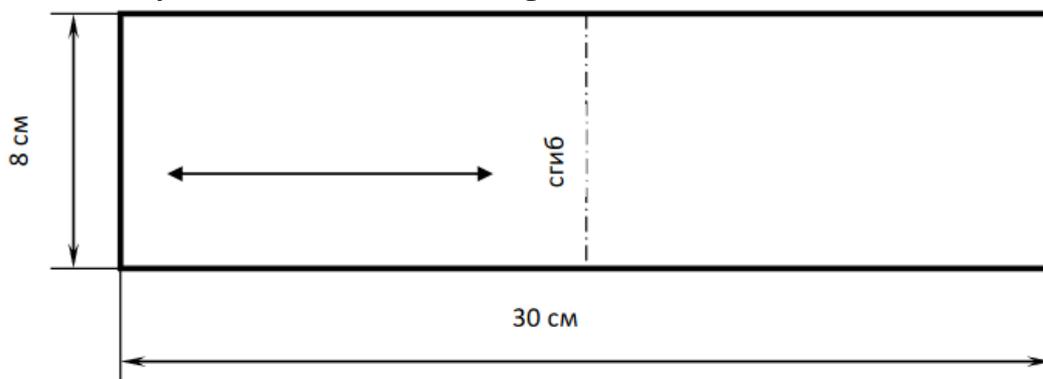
Основная деталь чехла, 1 деталь со сгибом
